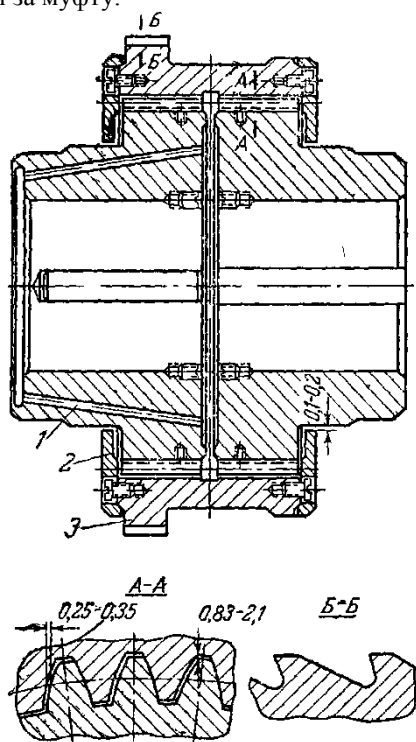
Подвижная зубчатая соединительная муфта.
